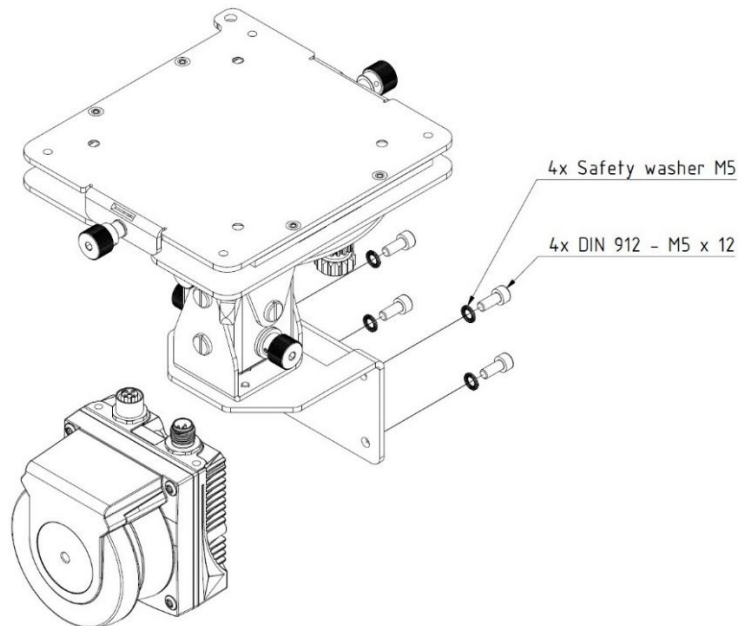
Explosionszeichnung Montage an Deluxe Mount
